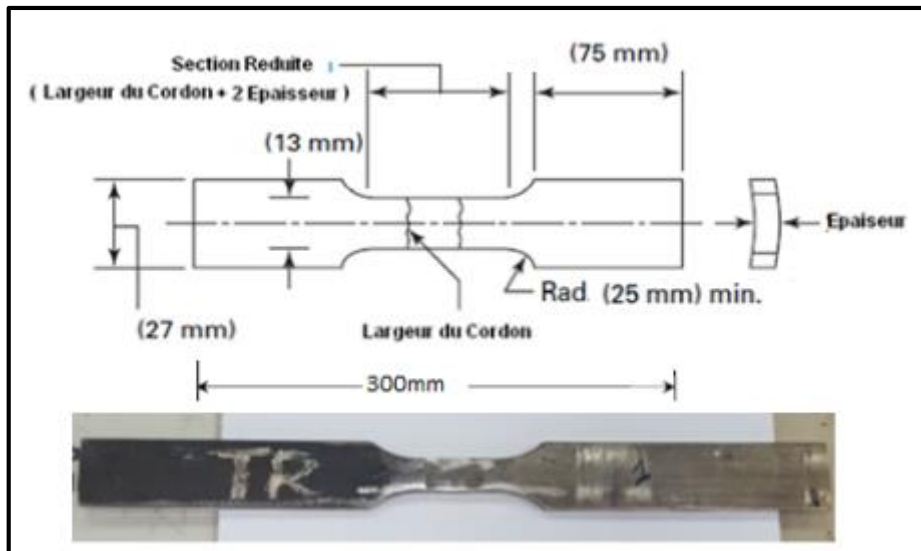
Forme et dimensions des éprouvettes de traction.
